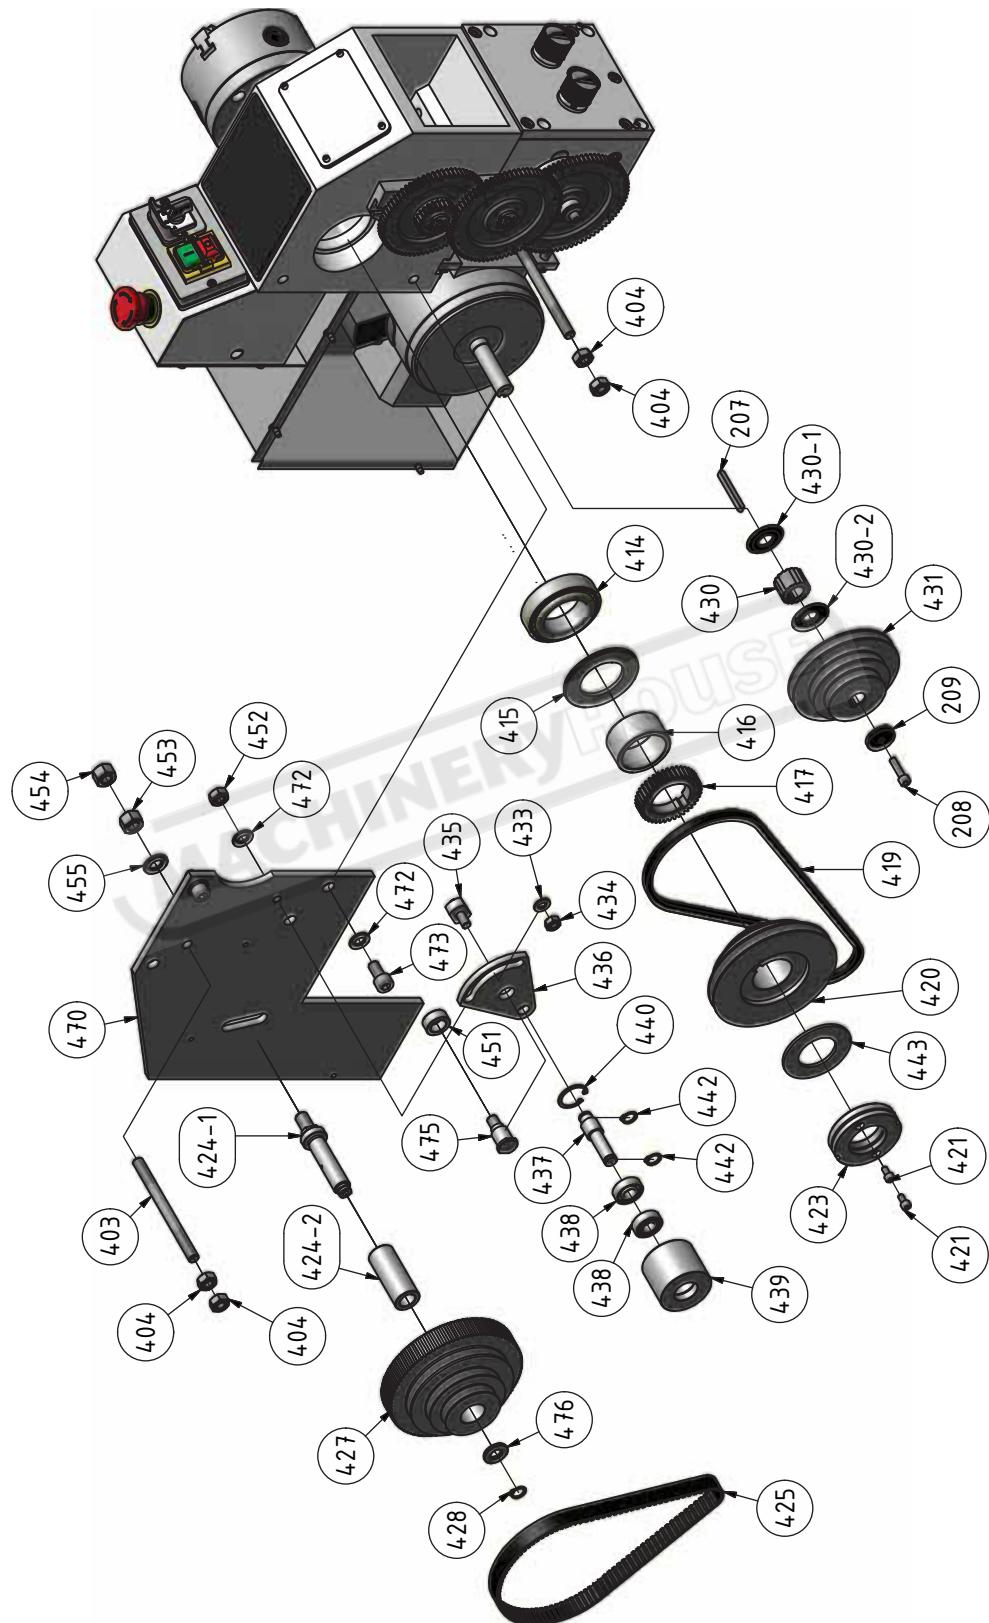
Spindelstock 1 von 2 - Headstock 1 of 2 - TU2506
